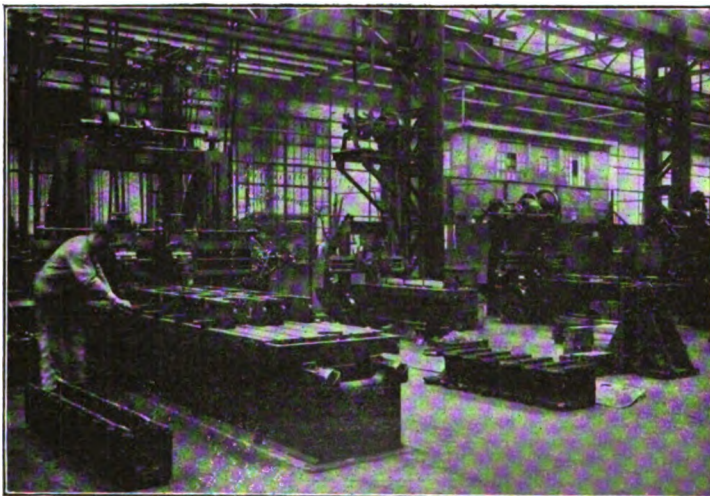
Bedienung mehrerer Hobelmaschinen durch einen Arbeiter.
